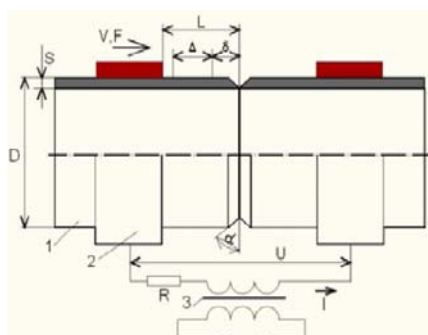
Схема процесса сварки оплавлением. 1 - Свариваемая конструкция, 2 - зажимы, 3 - сварочный трансформатор
